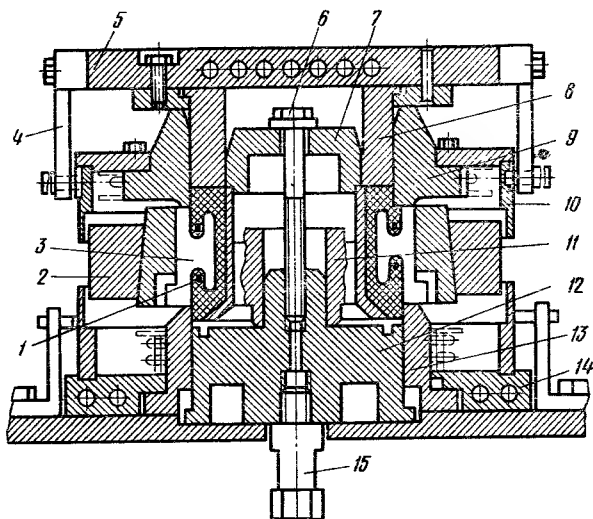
Пресс-форма для изготовления коллектора на пластмассе
